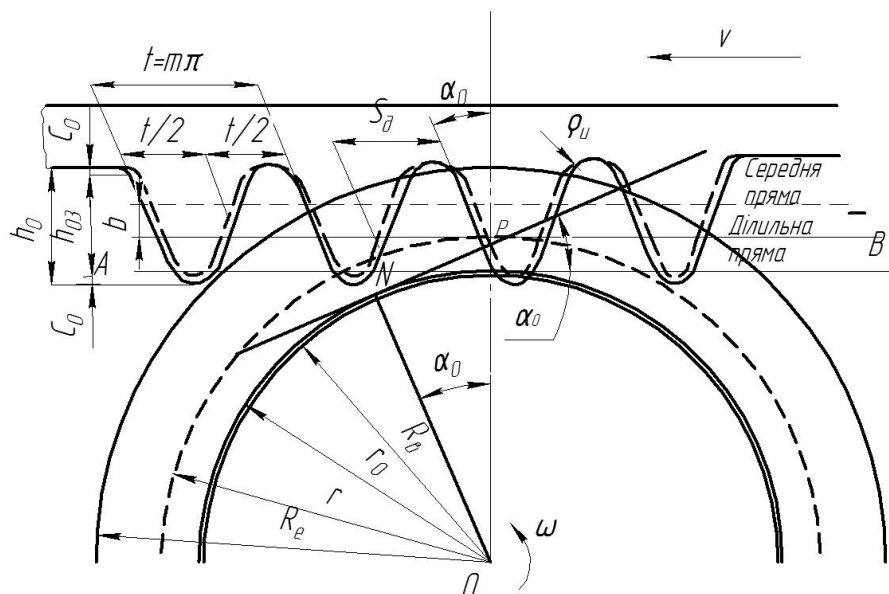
Виготовлення зубчастих коліс інструментальною рейкою
